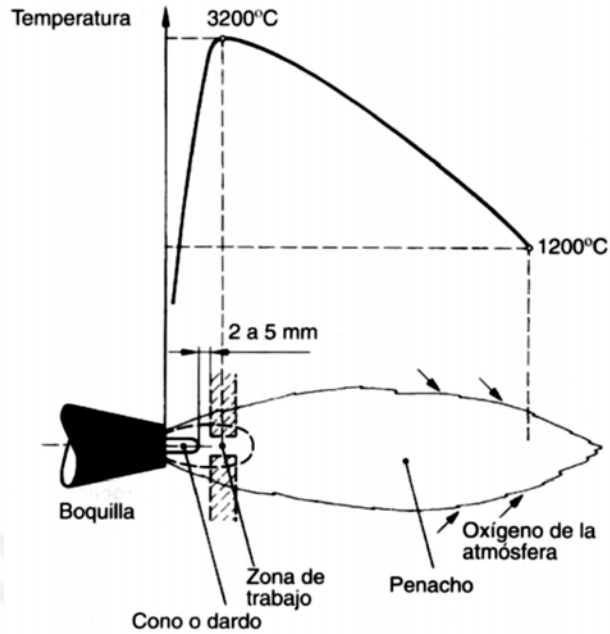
Llama del proceso de soldadura OFW [1]
